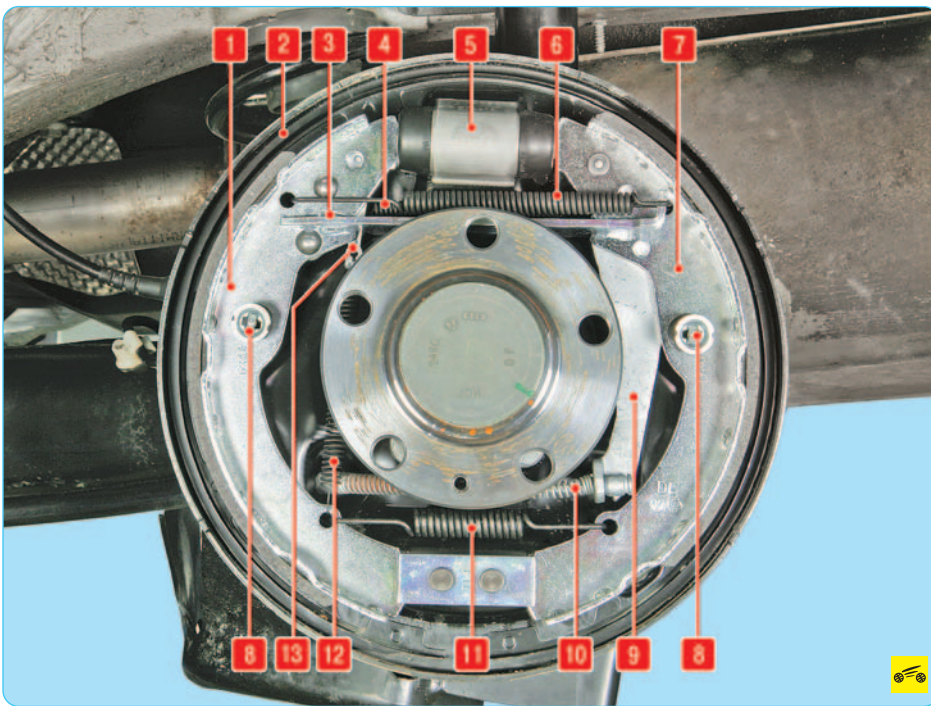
Тормозной механизм барабанного типа заднего колеса: 1 – передняя тормозная колодка; 2 – щит тормозного механизма; 3 – распорная планка; 4 – верхняя стяжная пружина; 5 – рабочий цилиндр; 6 – оттяжная пружина распорной планки; 7 – задняя тормозная колодка; 8 – опорная стойка; 9 – разжимной рычаг привода стояночного тормоза; 10 – трос привода стояночного тормоза; 11 – нижняя стяжная пружина; 12 – пружина механизма регулировки зазоров; 13 – клин механизма регулировки зазоров
